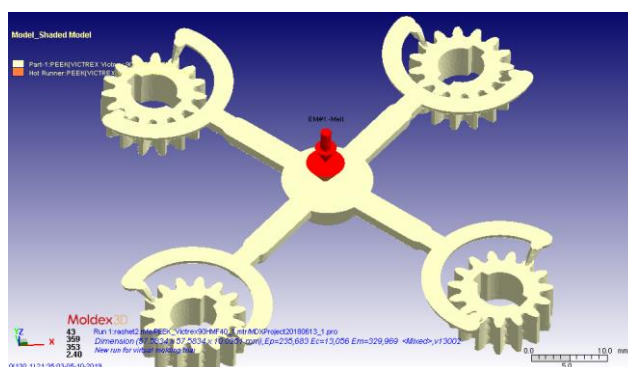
Представление литниковой системы с двумя точками подвода расплава в Moldex 3D
